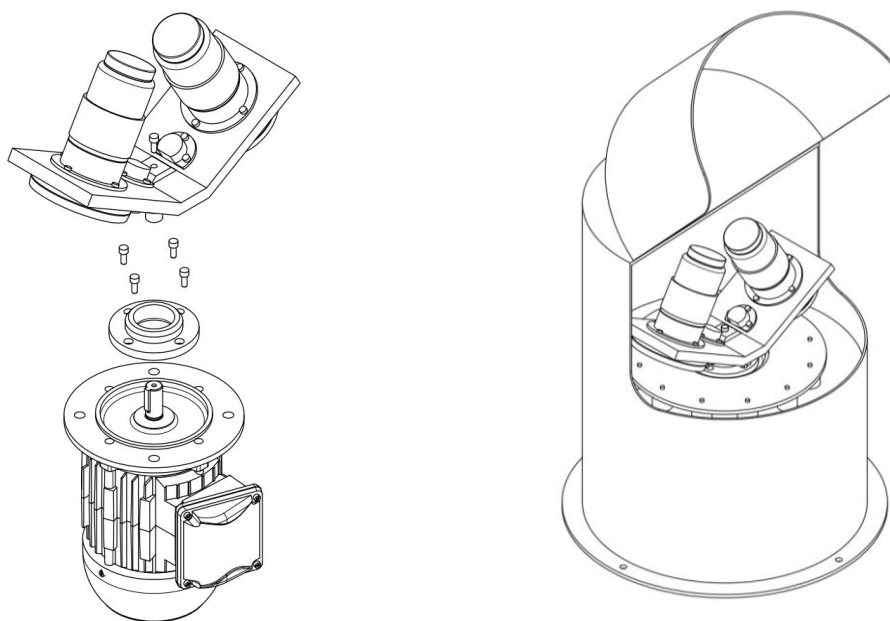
Projeto virtual do equipamento. (a) Vista explodida da configuração de mistura. (b) Conjunto completo na condição de moagem.
